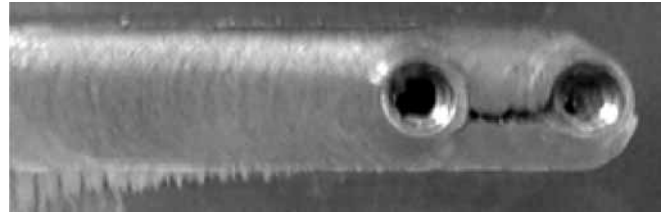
Подварка несплавления повторным проходом сварки трением с перемешиванием
